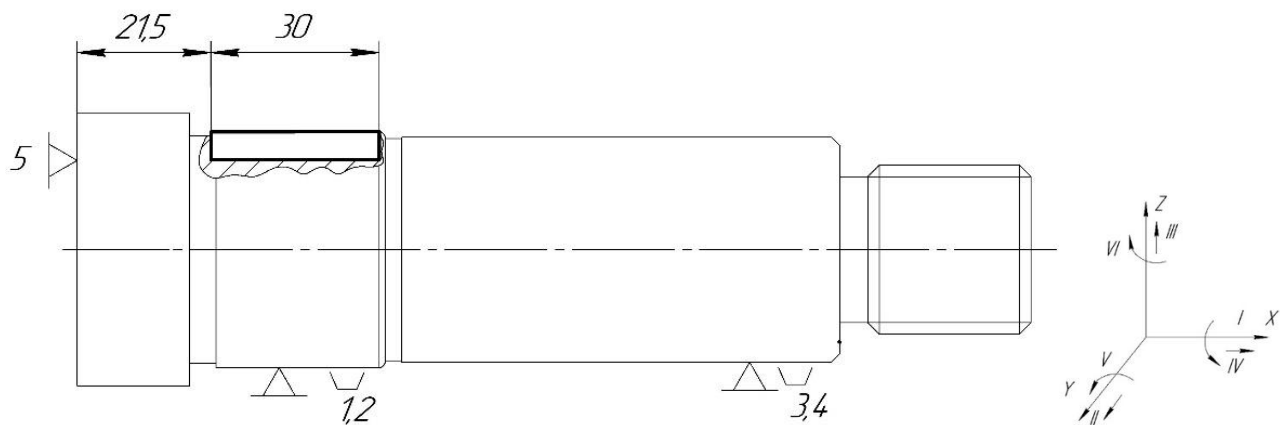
Схема базування, закріплення заготовки при операції 030 – Шпонково-фрезерна
